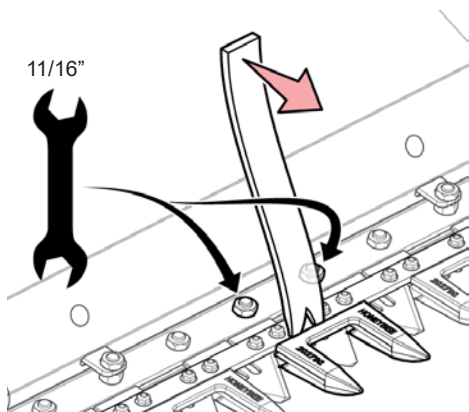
Смещайте сдвоенный палец вперед во время затяжки крепежных деталей
